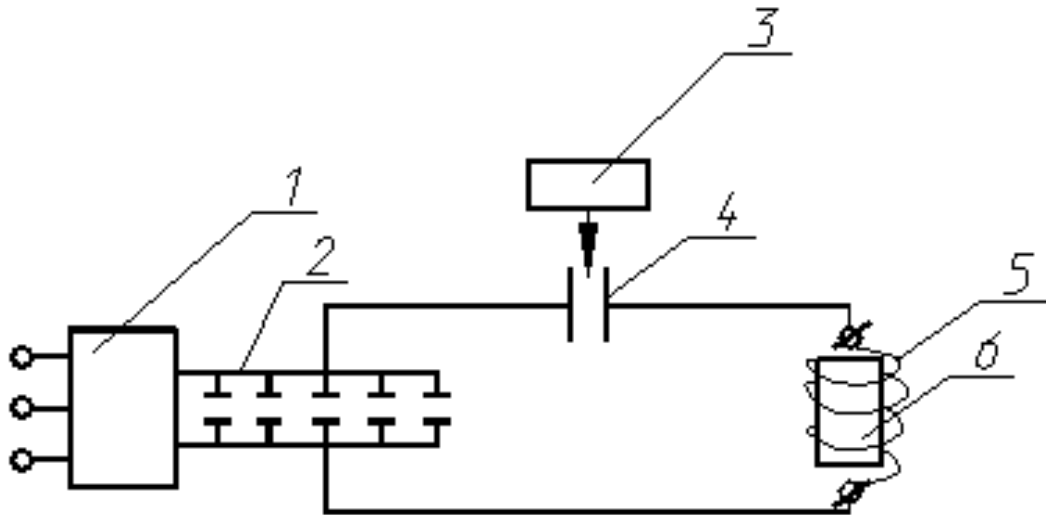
Штампування електромагнітне: 1 – зарядний пристрій, 2 – емнісний накопичувач, 3 – регулятор напруги, 4 – 3-х електродний розрядник, 5 – індуктор, 6 – заготовка
